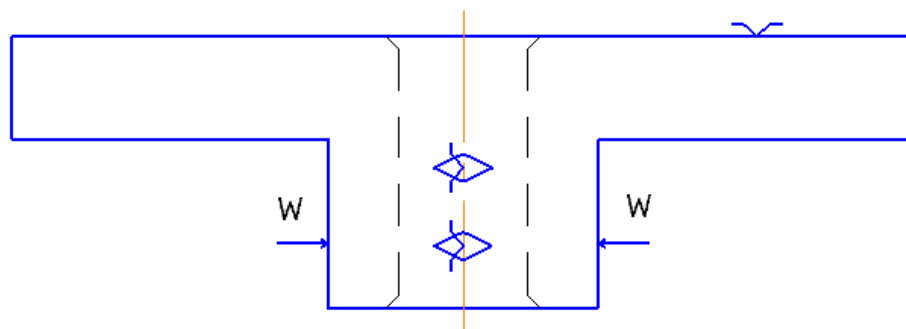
Принципиальная схема зажима заготовки в приспособлении с указанием мест приложения силы зажима.
